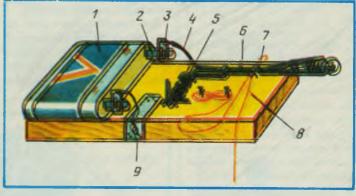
Жерлица в собранном виде: 1 — батарейка; 2 — контакты батарейки; 3 — клемма с припаянным проводом; 4 — провод МГШВ; 5 — скобы из гвоздей для крепления сторожка к деревянной планке; 6 — сторожок; 7 — скобы взводно-спускового механизма; 8 — леска;
